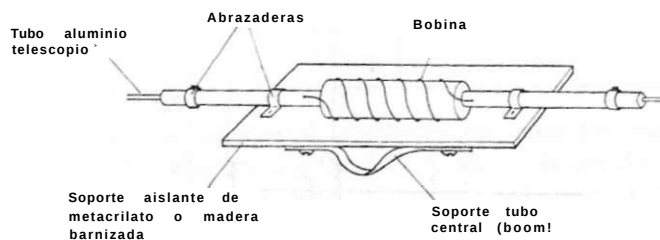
Detalle constructivo de la antena Yagi con acortamiento eléctrico.
